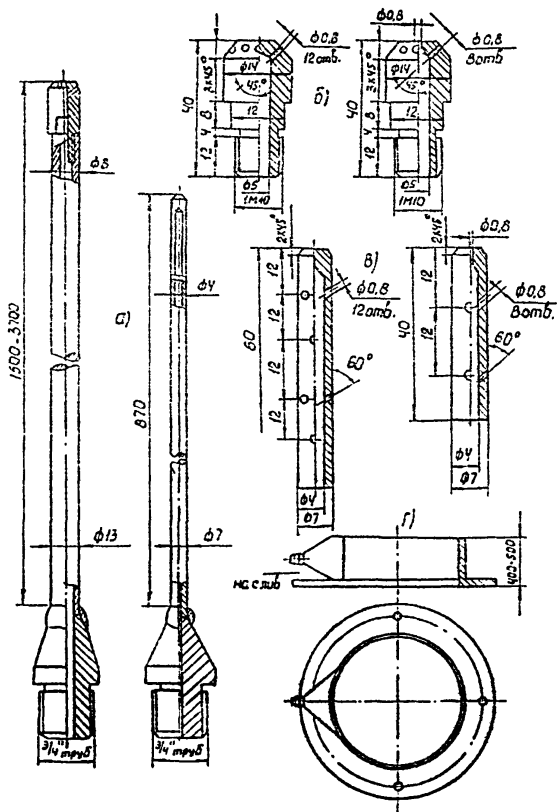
Негабаритные устройства, необходимые для гидромеханической очистки охладителей:
